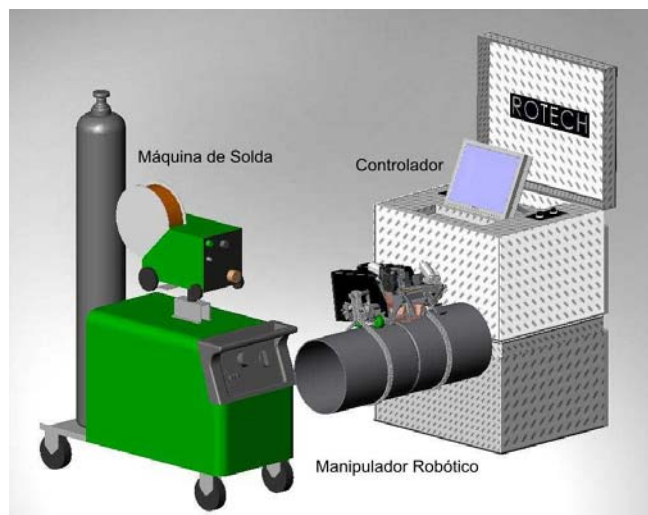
Sistema robotizado para soldagem orbital de tubulações.
